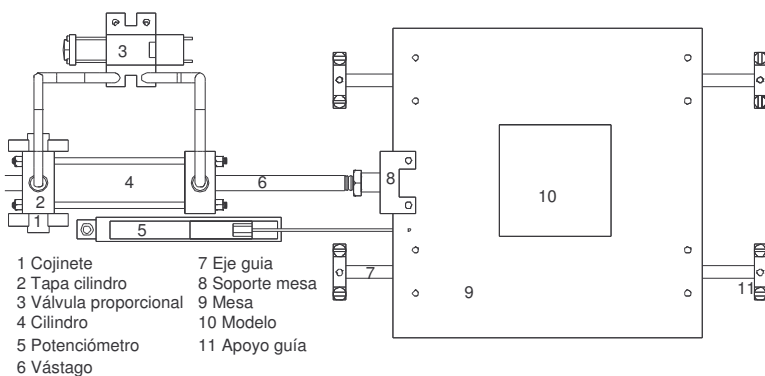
Detalle vistas superior y perfil de los componentes del grupo hidráulico de accionamiento.
